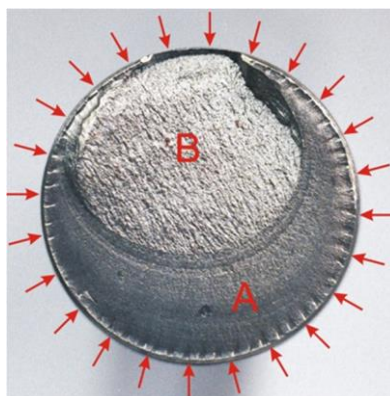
Vzhľad typického únavového lomu a detail striácií
